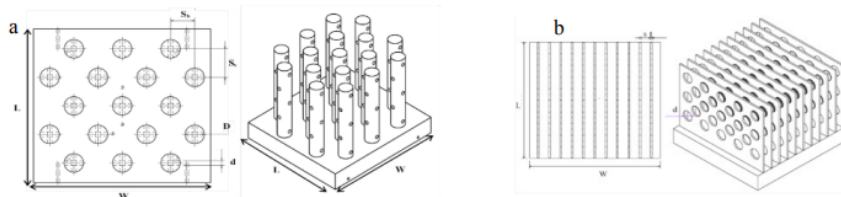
Modelos Catia (a) aletas perforadas, vista superior (izquierda) Vista isométrica (derecha), (b) placa plana perforada, vista superior (izquierda) vista isométrica (derecha) [35].
